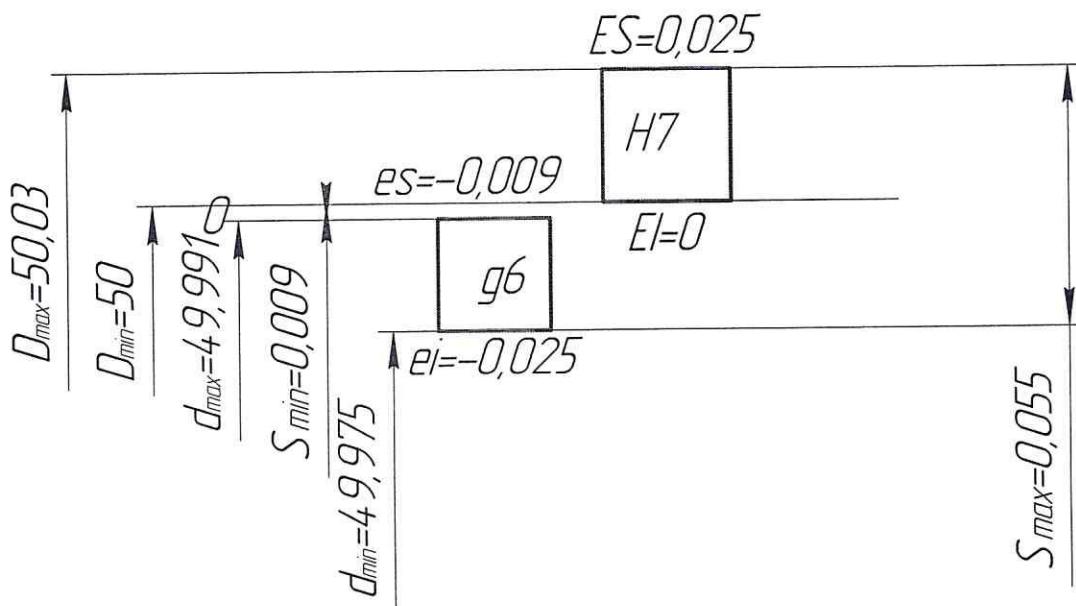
Схема расположения полей допусков отверстия и вала
